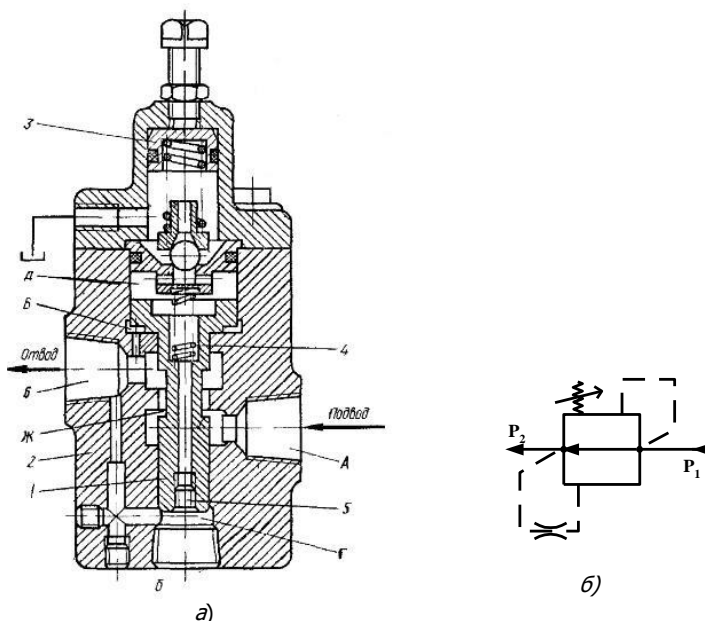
Редукционный клапан Г57-1: *а* – конструктивная схема;
